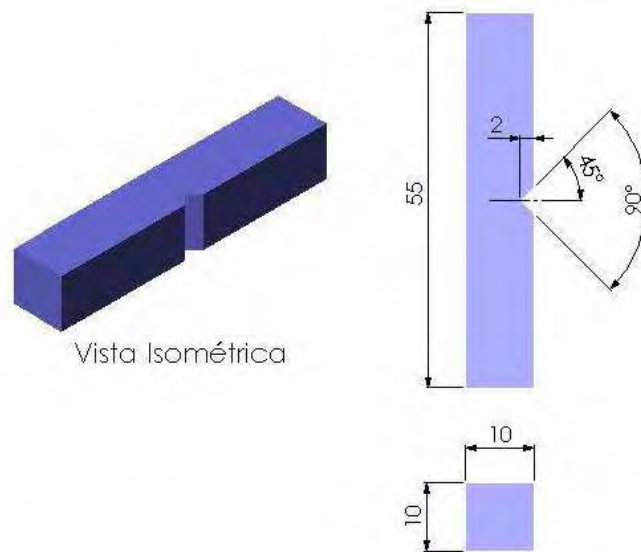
Dimensões dos corpos-de-prova para ensaio de impacto (dimensões em mm) ASTM A370 (adaptada de ELISEI, 2008)
